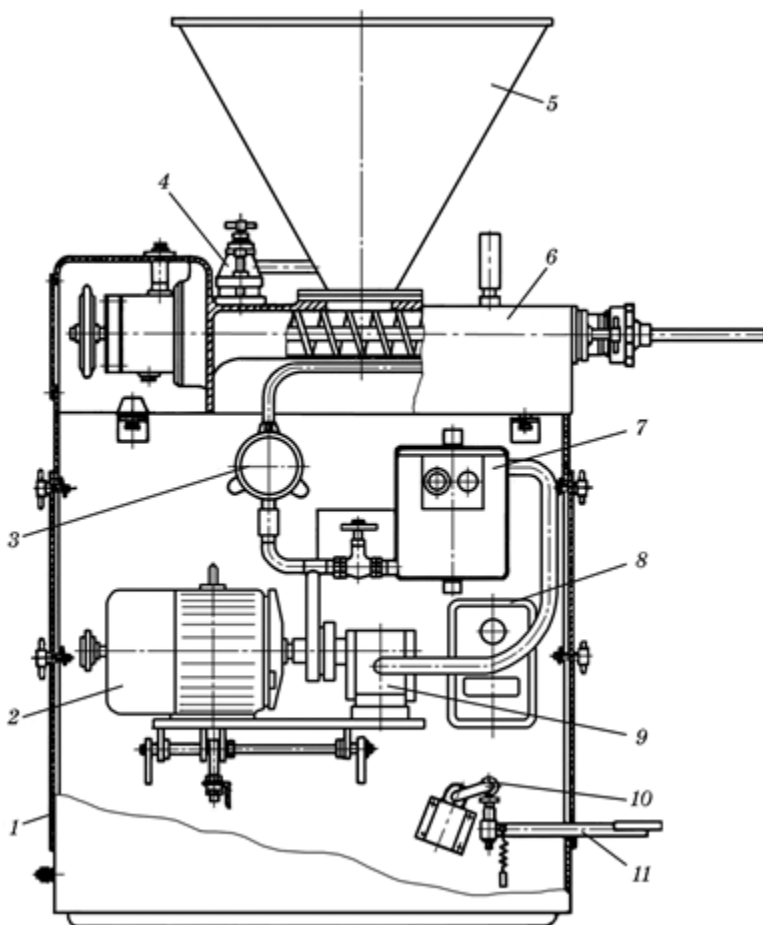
Шприц вакуумний двоцільковий ФШ2-ЛМ:
